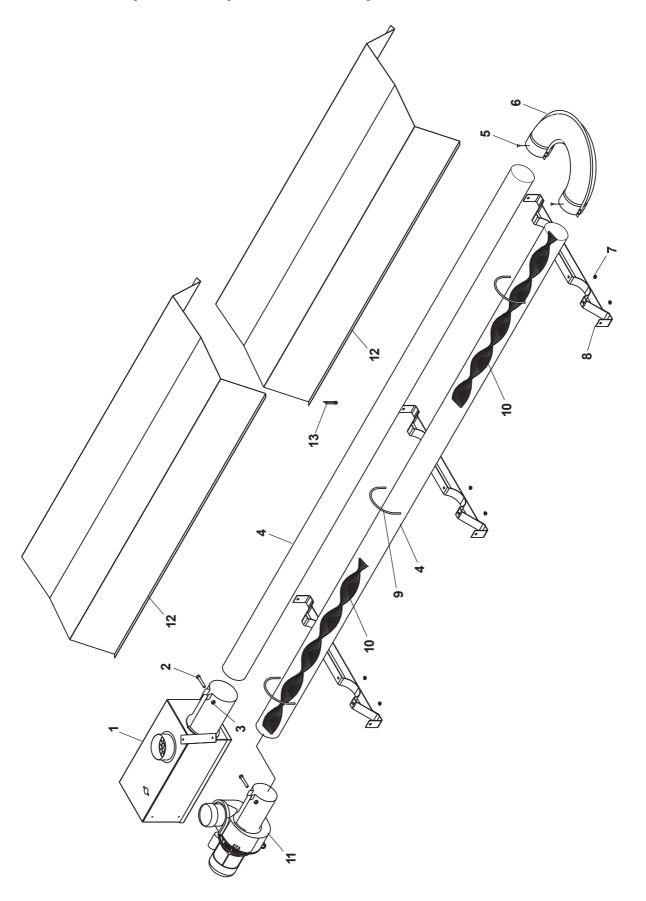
Деталировка излучающего модуля INFRA 9BL
